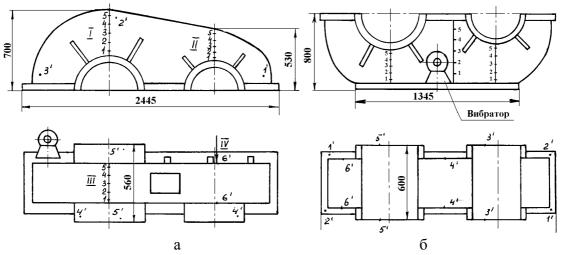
Схема расположения базовых точек для замера деформаций на крышке (а) и корпусе редуктора (б)
